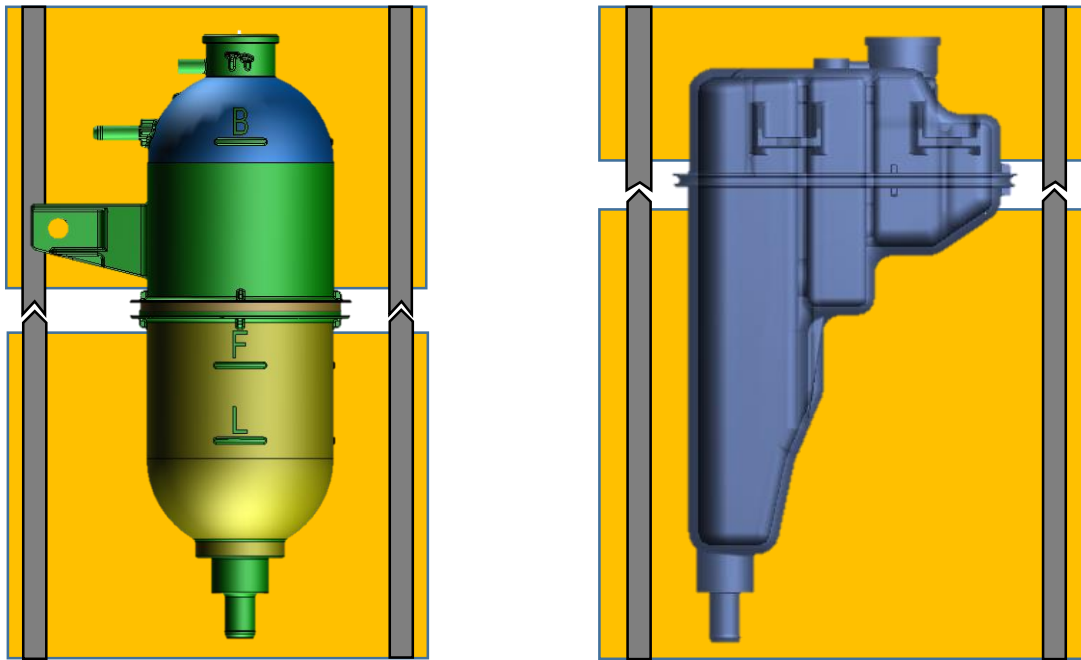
Vista de piezas en la matriz de soldadura cerrada
